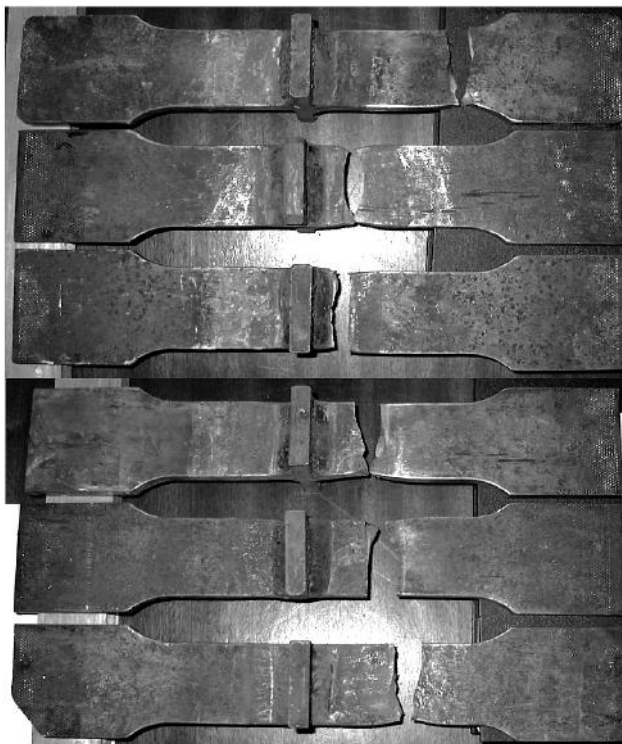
Общий вид разрушенных образцов таврового сварного соединения стали 10ХСНД после испытаний на усталость в коррозионной среде.
